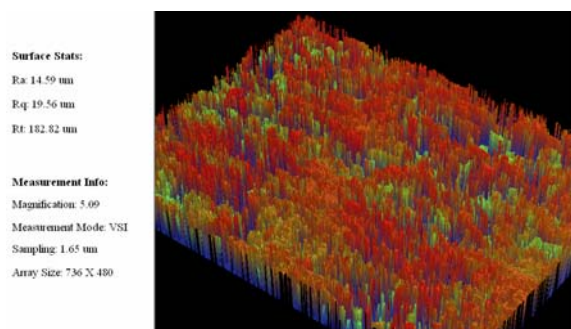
2.33 : Exemple de relevé topographique d'une surface usinée par un outil revêtu de CrN après 110 m d'usinage
